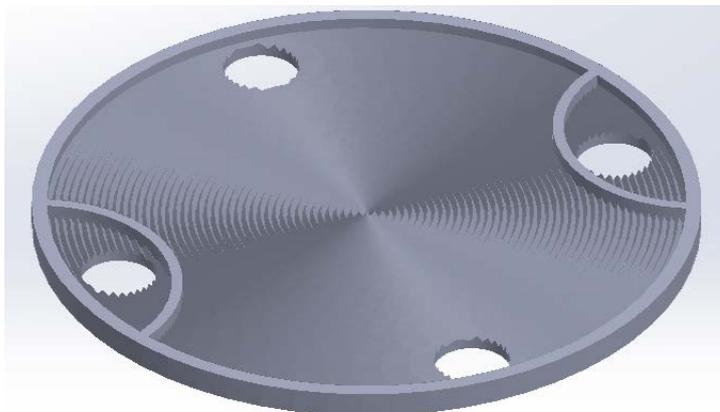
Placa impressa do projeto de trocador de placas, realizado pelo grupo 6.
